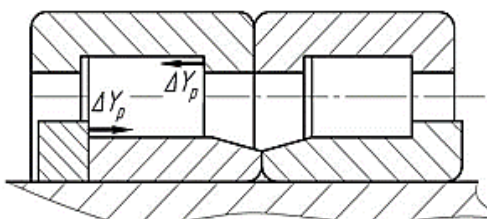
Схема передачи рамной силы цилиндрическим подшипникам
